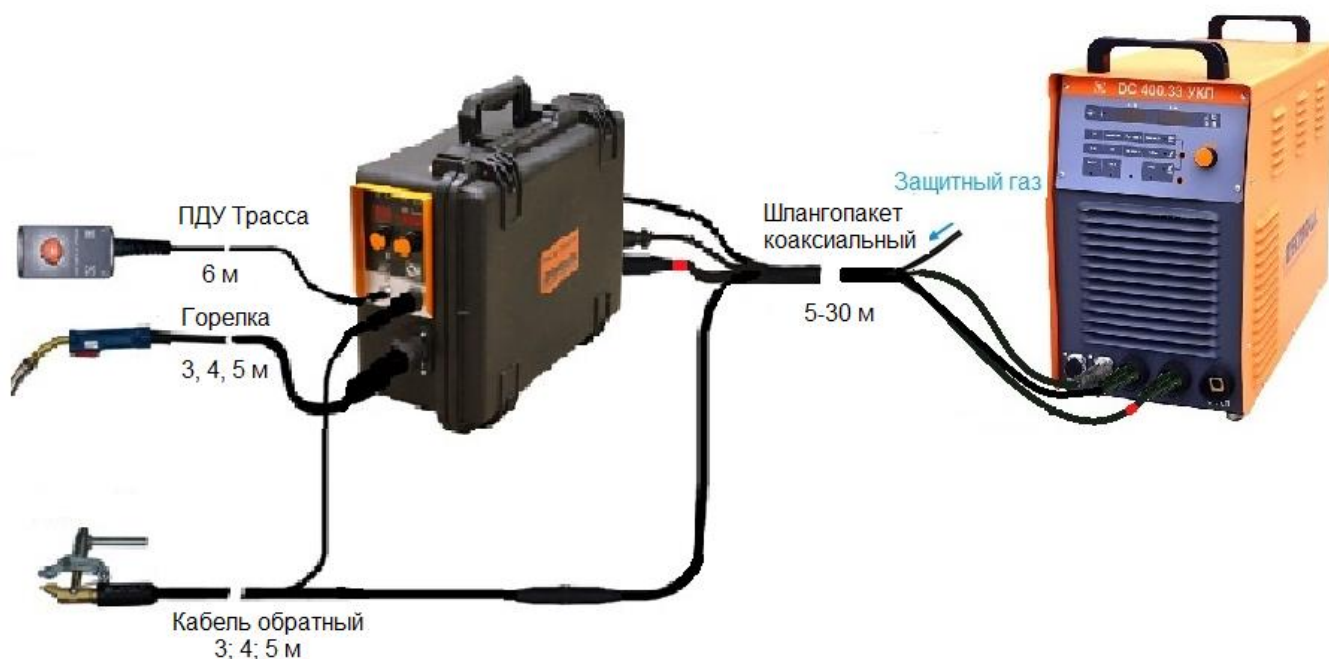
Схема сборки при сварке в режиме УКП
